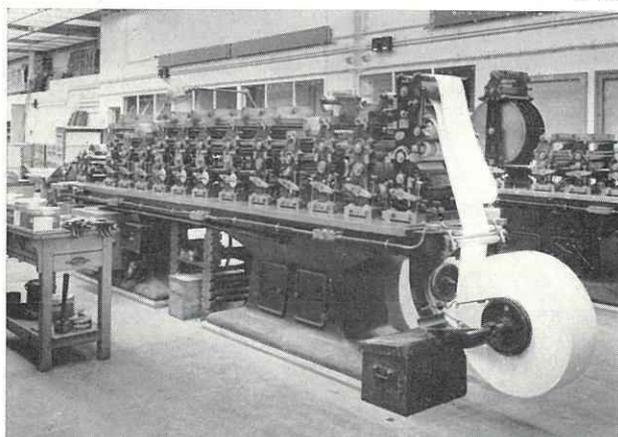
Ensemble d'une rotative assurant la fabrication des carnets de tickets (côté embarreur)
